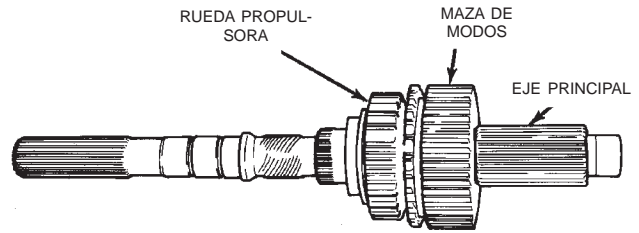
Instalación de conjunto de horquilla y maza de posiciones
